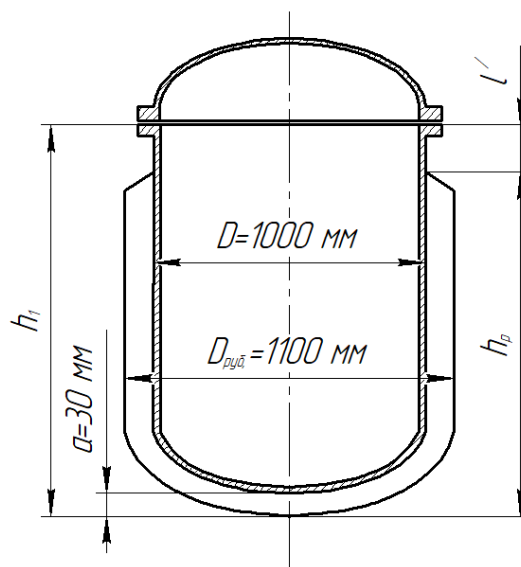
Конструктивный расчет рубашки реактора: h_p – высота рубашки с учетом днища реактора; l – конструктивная величина
